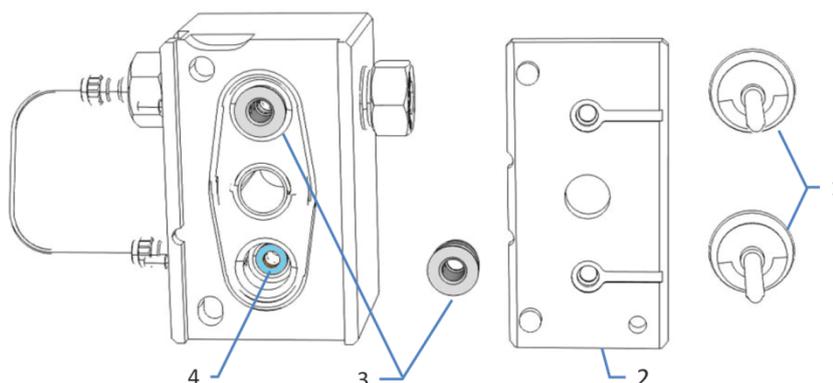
Tête de pompe, plaque de rinçage des joints retirée
